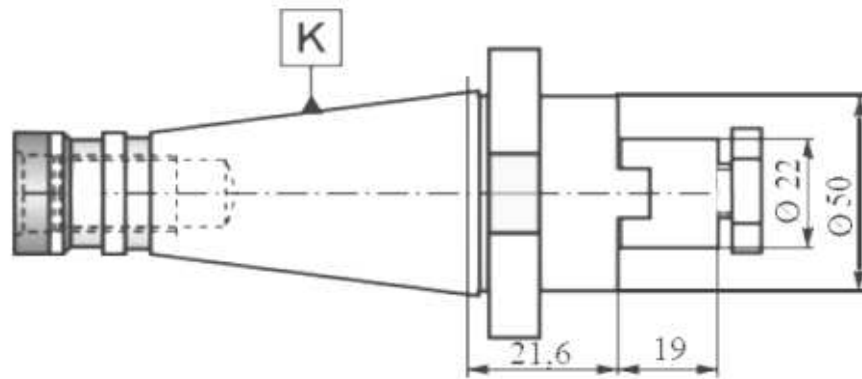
оправка для торцовых фрез АК 155.M.0.50.025.22
